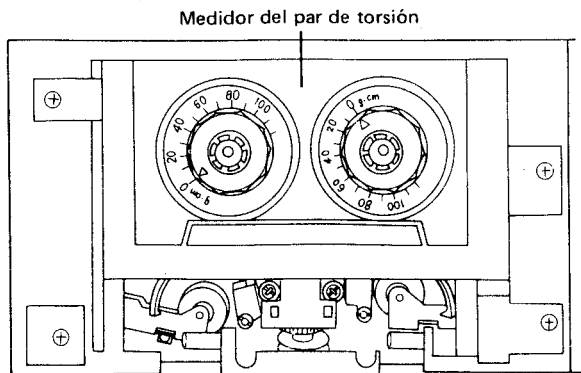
Ajuste del par motor de bobinado en el modo de reproducción
